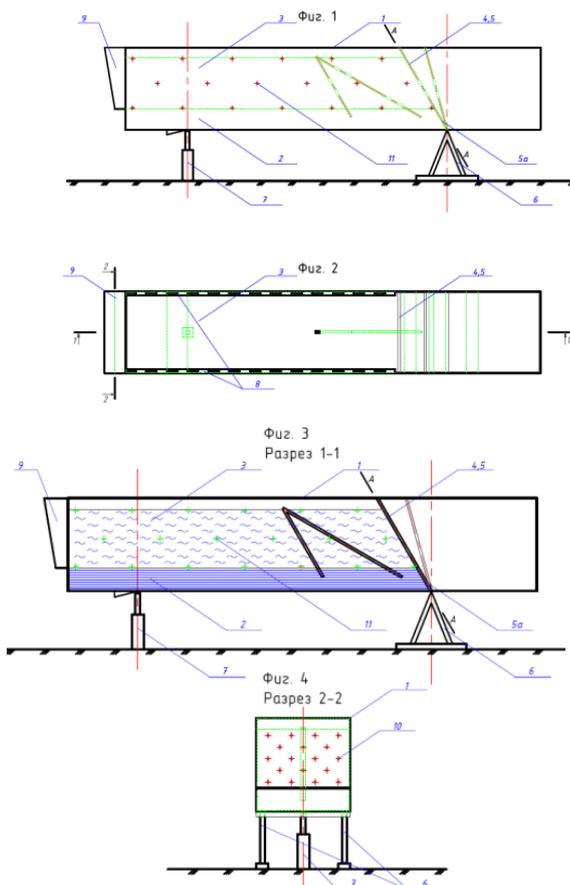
Конструкция стенда для проведения испытаний Фиг.1 – вид сбоку, фиг.2 – вид сверху, фиг.3 – разрез продольный, фиг.4 – разрез поперечный
